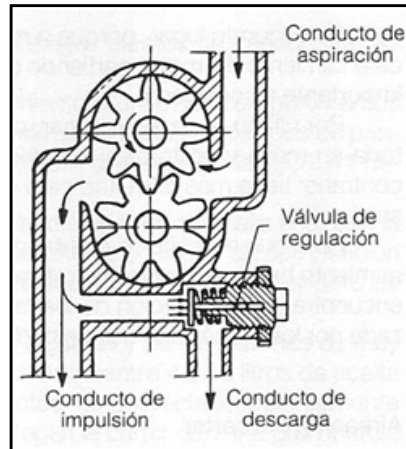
Esquema de una bomba de engranajes dotada de válvula de regulación para el ajuste de la presión
